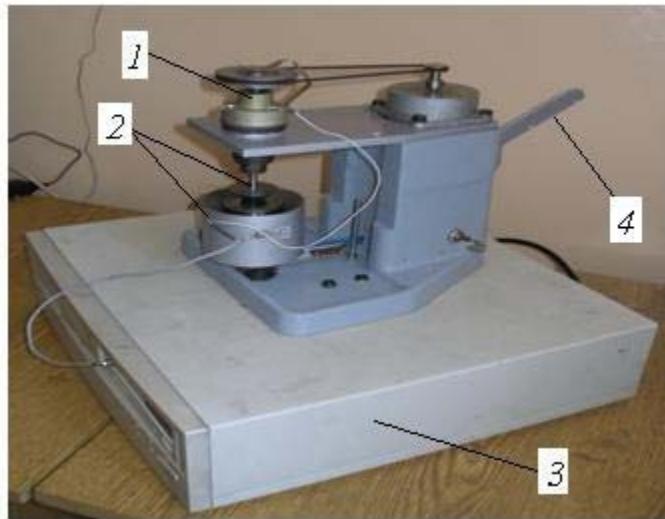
Внешний вид стенда для входного контроля подшипников качения: 1 – приводная установка; 2 – конические оправки для закрепления подшипника; 3 – измерительно-управляющий комплекс; 4 – рычаг нагрузжения
